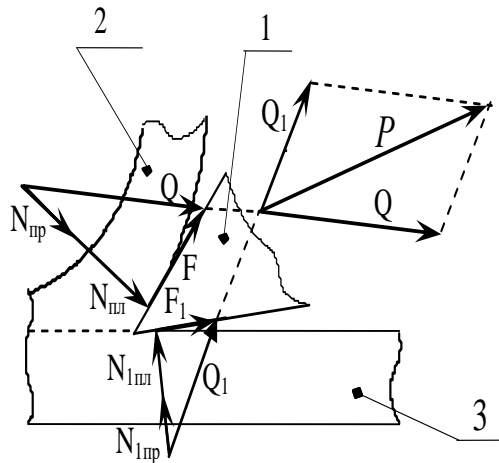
Схема сил, що діють на різальний клин (лезо) інструмента
